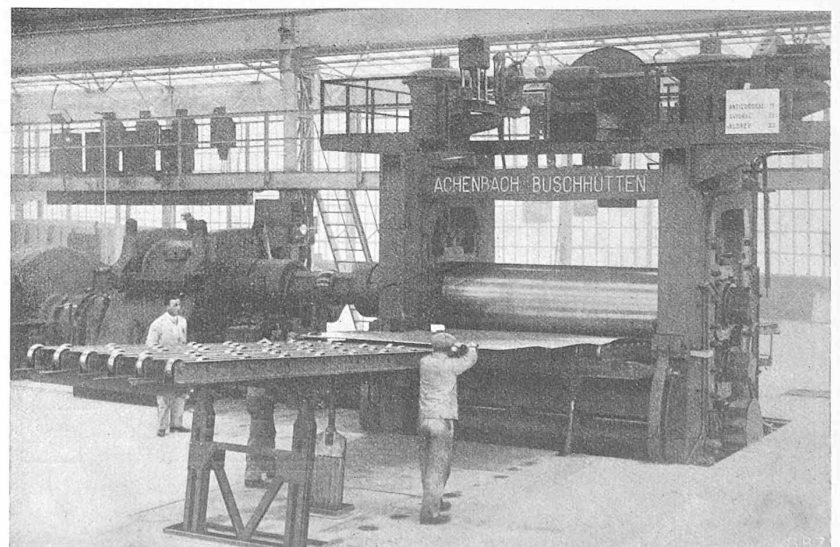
Trio-Walzwerk für Konstruktionsbleche.
